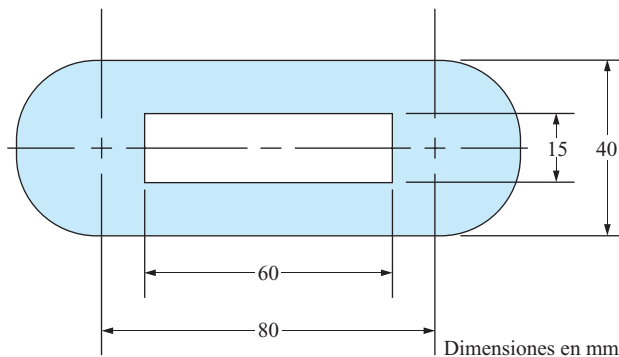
Miembro corto sometido a compresión del problema 1-56.
